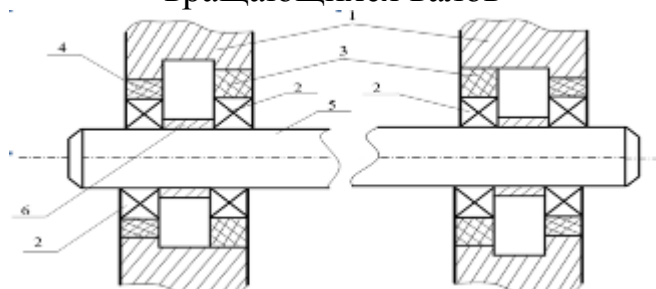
Подшипниковые опоры с упругими элементами вала пильного цилиндра
